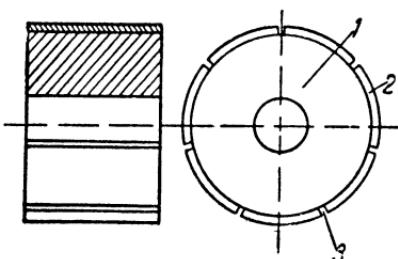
Цилиндрический коллектор самодельного двигателя.
